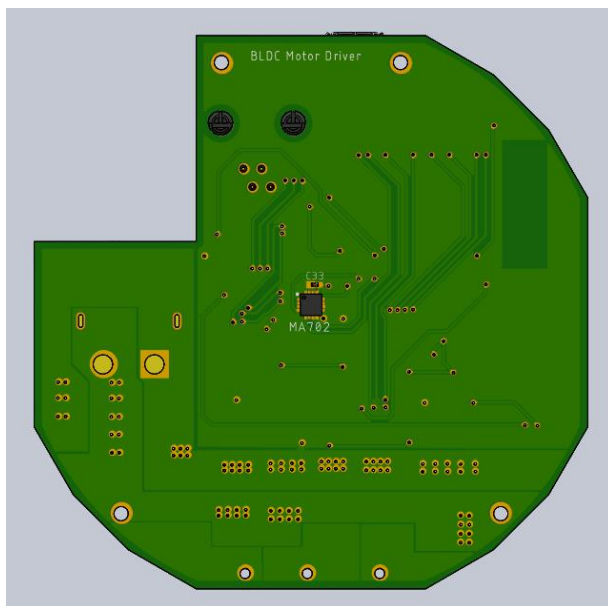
Vista inferior de la PCB (Font: Ernest Porqueras)
